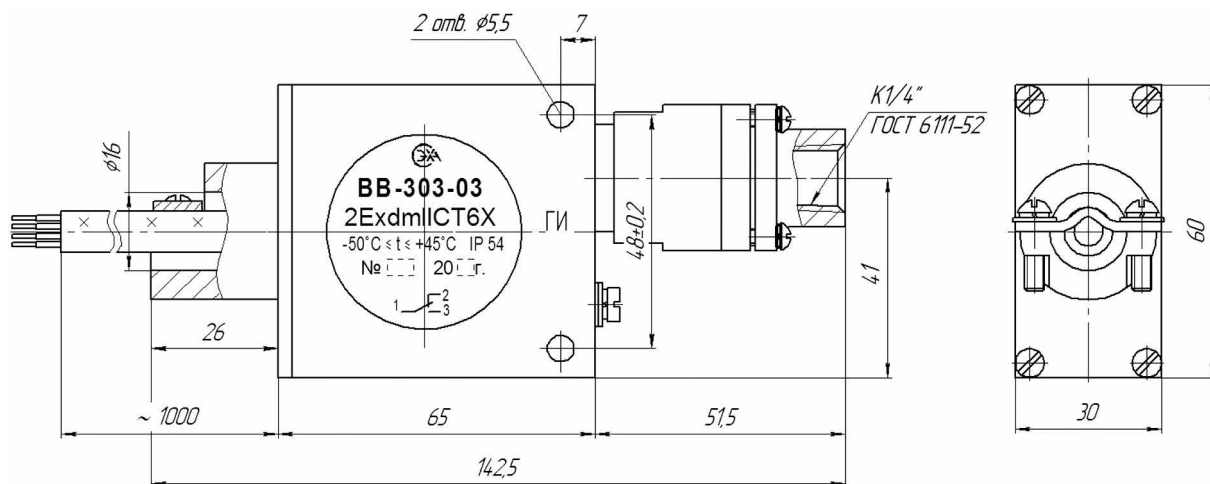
г. Габаритные и установочные размеры ВВ-303-03
